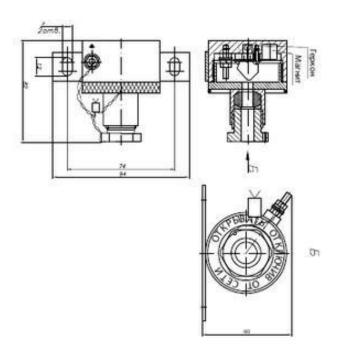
Габаритные и присоединительные размеры МГДУ КП модели 03.
